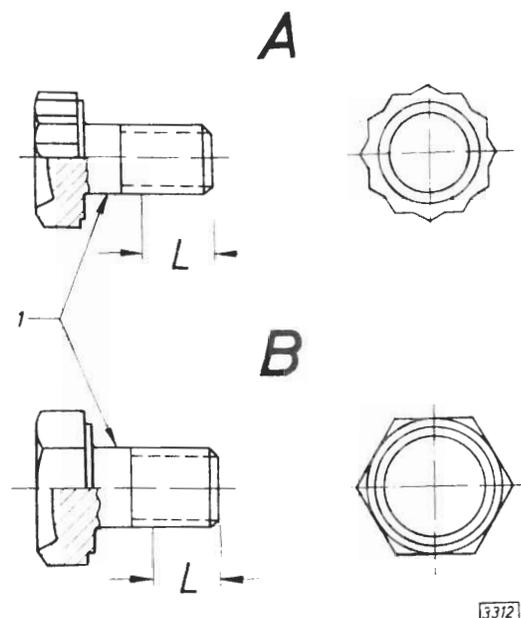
Ausführungen von Schrauben zur Befestigung des Tellerrades an das Ausgleichgehäuse
